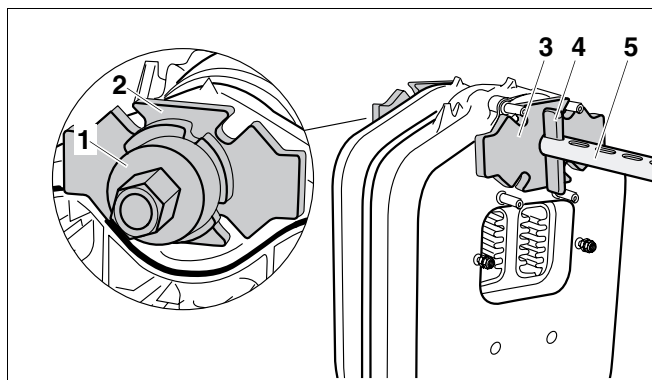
Установка стяжного инструмента на верхней ступице котла
